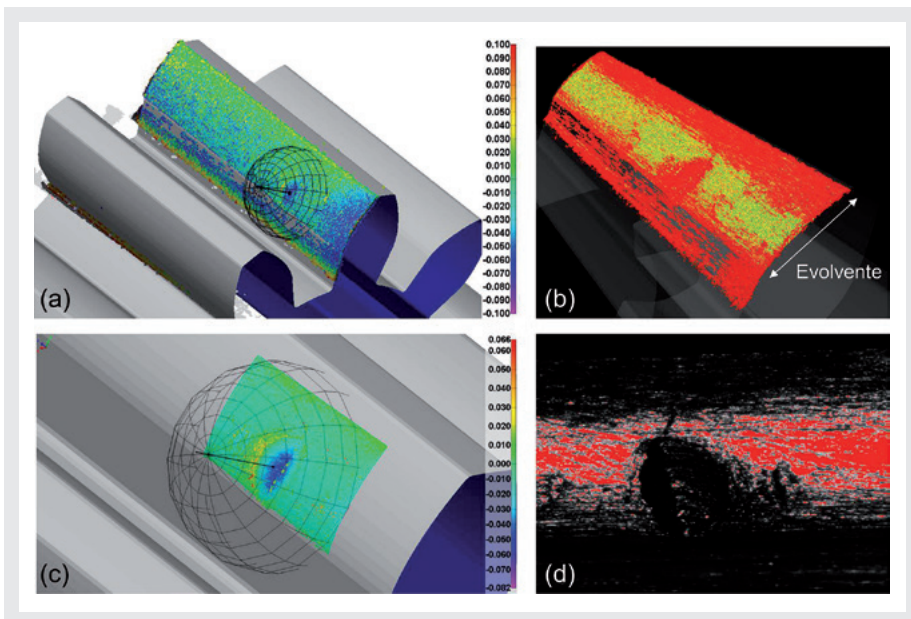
Multiskalige Inspektion einer Delle in einer Zahnflanke. In einer Übersichtsmessung (a) wurde die Flanke zunächst mit der mikroskopischen Streifenprojektion und 1.0x Vergrößerung abgetastet. Um den Defekt besser bewerten zu können, wurde schließlich die Evolvente mit drei Einzelmessungen mit der 2.5x Vergrößerung detaillierter aufgenommen (b). Die Bilder (c) und (d) zeigen schließlich Detailtopografie- und Intensitätsdaten der Delle mit der 5.0x Vergrößerung
